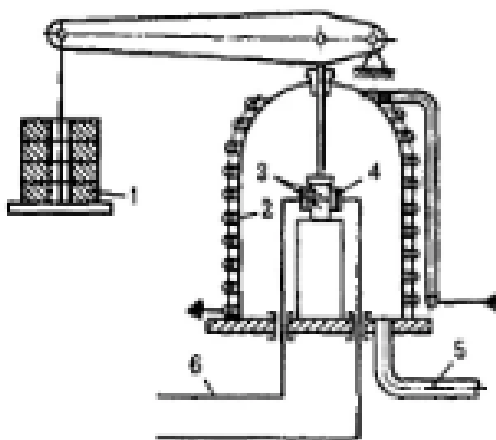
Диффузионная сварка в вакууме
